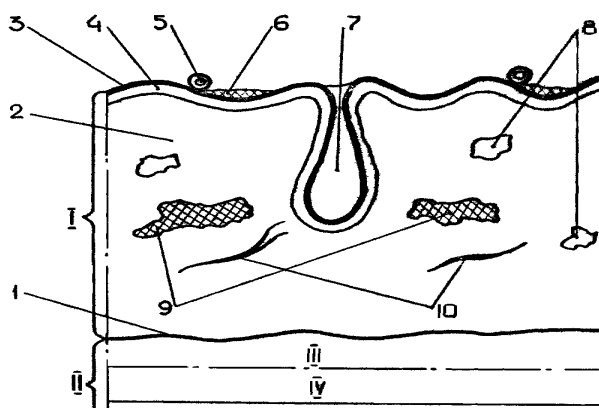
Схема строения участка детали с наплавленным слоем: I – наплавленный слой; II – основной металл детали; III – зона термического влияния; IV – металл детали с неизменными свойствами; 1 – поверхность сплавления; 2 – металл наплавленного слоя; 3 – поверхность наплавленного слоя; 4 – окисная пленка; 5 – капли застывшего металла; 6 – шлаковые включения; 7 – поры, выходящие на поверхность; 8 – поры, не выходящие на поверхность; 9 – неметаллические включения; 10 – трещины
